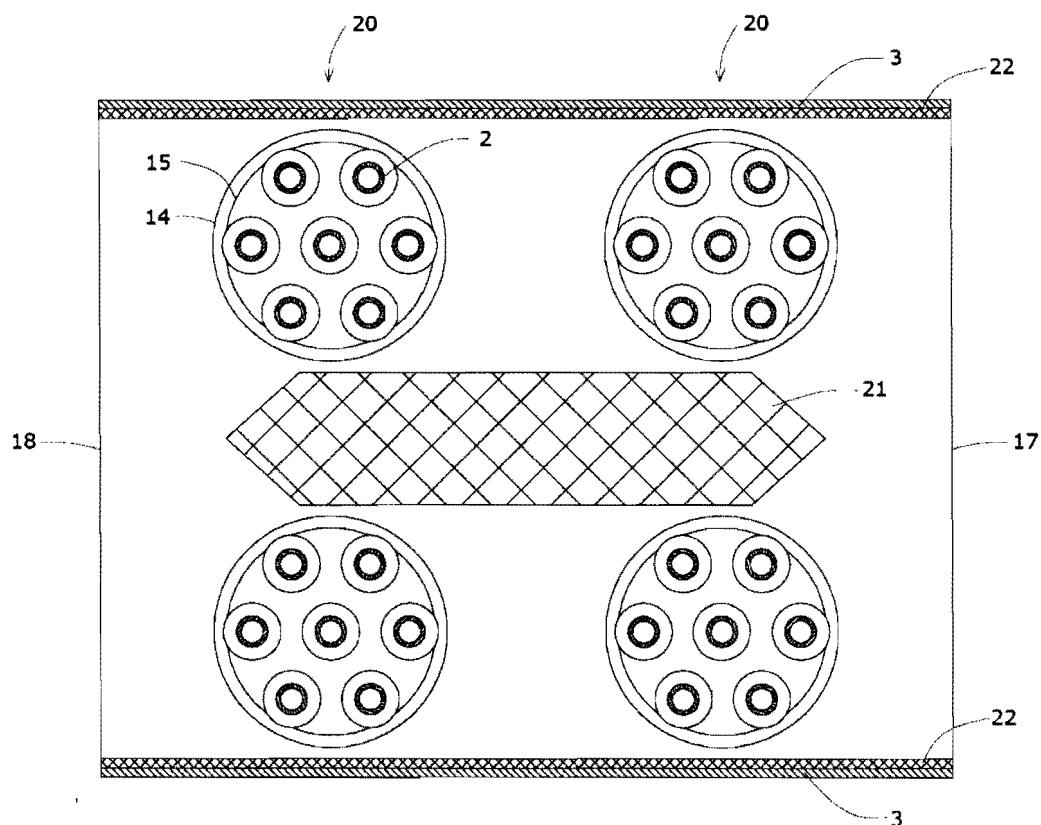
Sectiune orizontala B-B prin schimbatorul de caldura
